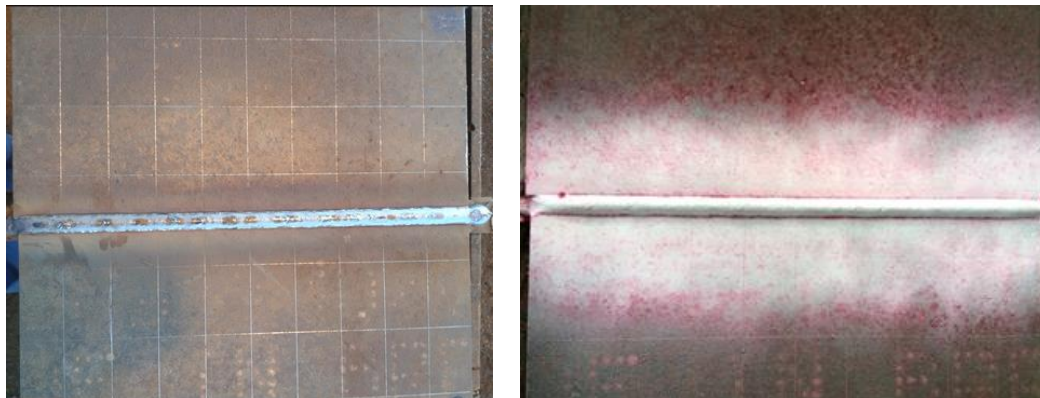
Dimensionais do cordão de solda - Condição de soldagem S2
